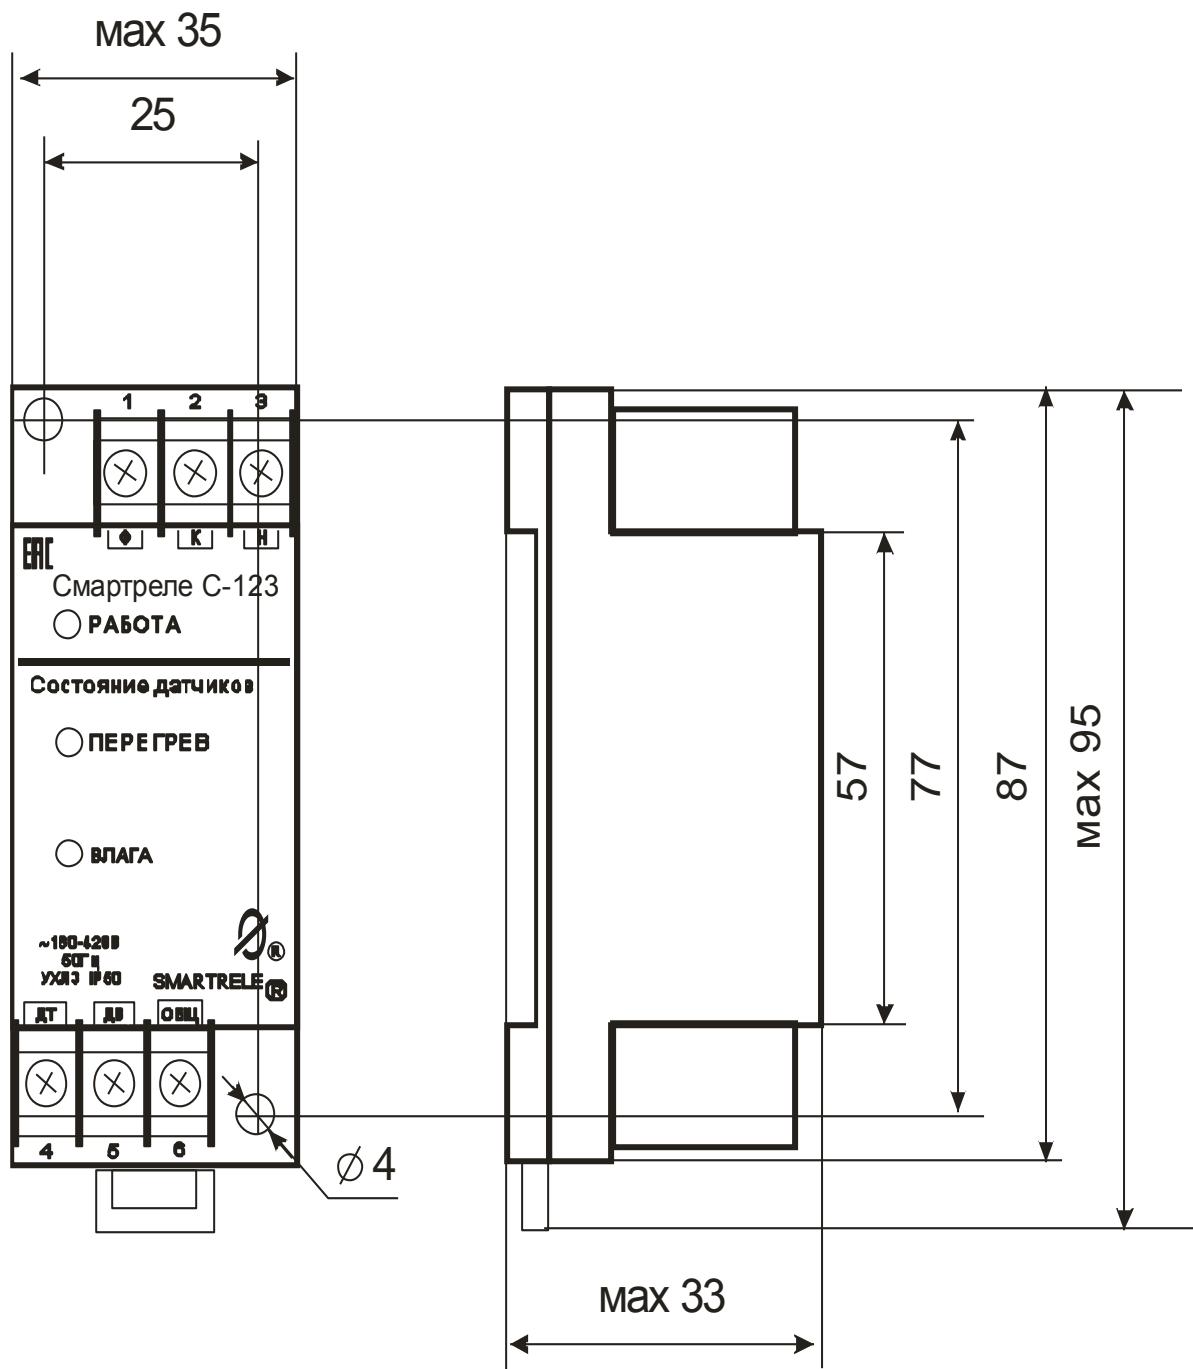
внешний вид, габаритные и установочные размеры реле
